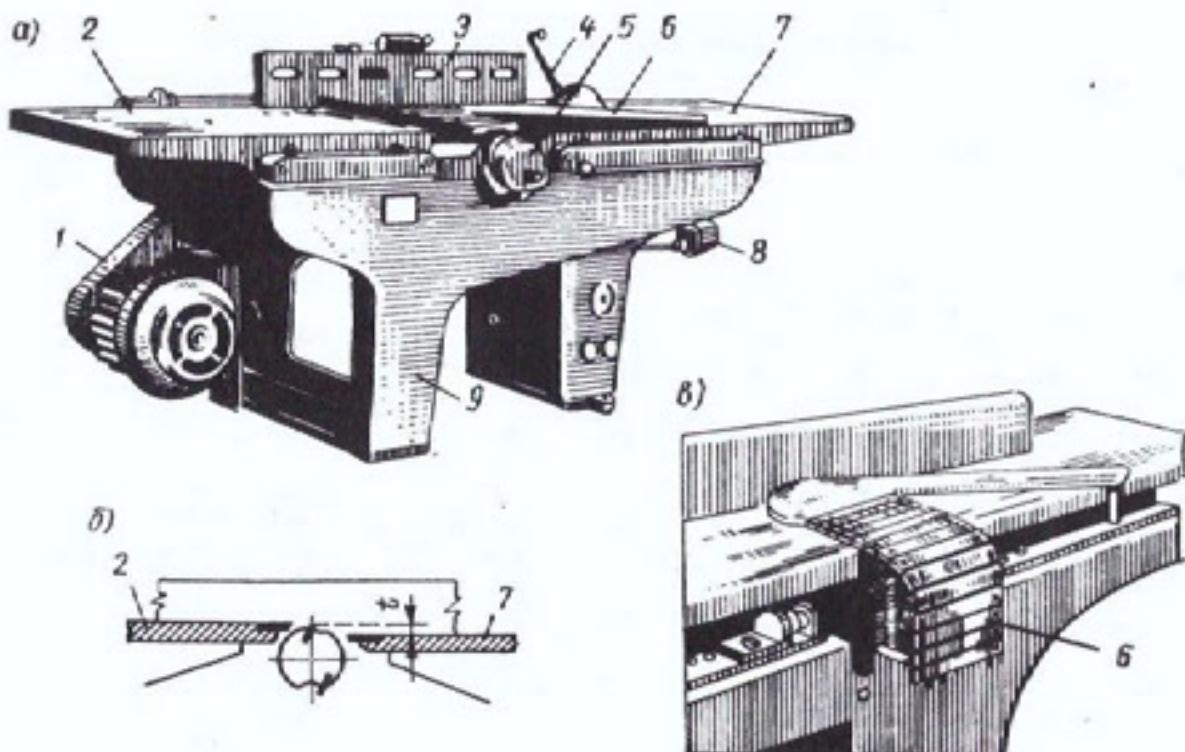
Фуговальный станок СФЗ-2: *а* — общий вид; *б* — схема строгания; *в* — установка веерного ограждения.
